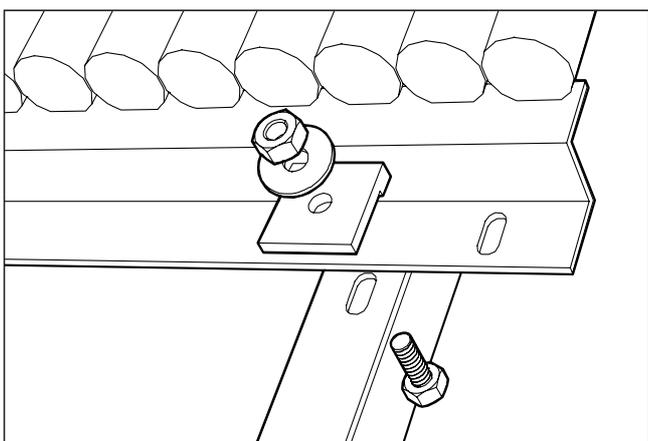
Закрепить основание коллектора с помощью скоб крепления и болтов М10 с гайками и шайбами так, чтобы выступ клеммы с выбитой стрелкой показывал в направлении коллектора.
